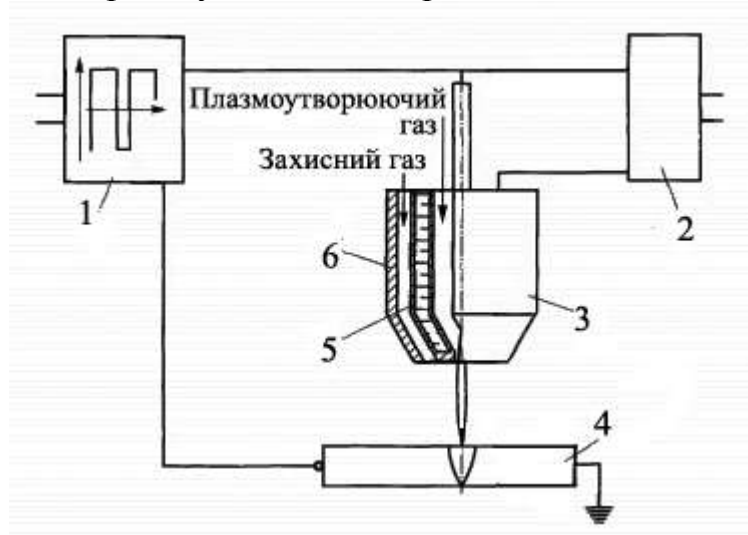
Схема установки для зварювання алюмінієвих сплавів асиметричним струмом прямокутної форми:
